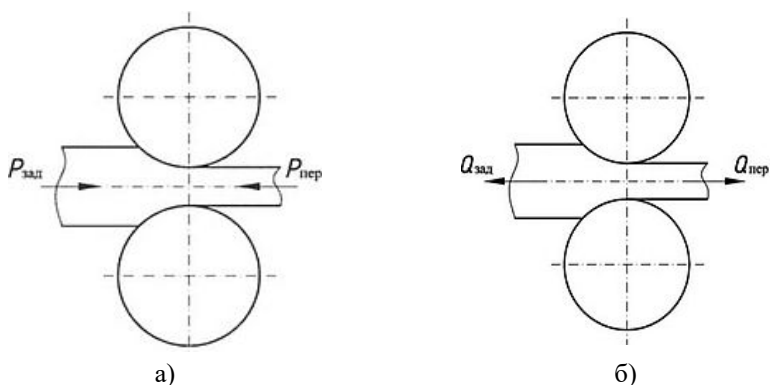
Схема прокатки: а – з підпором; б – з натягом
